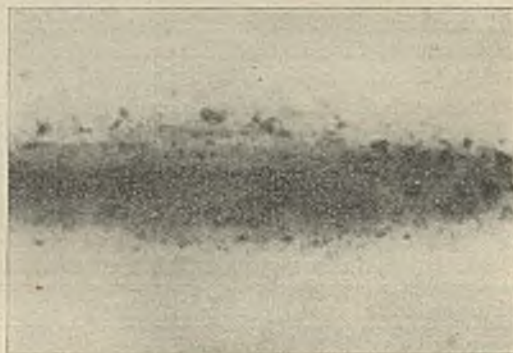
Röntgenaufnahme einer Elektroschweißnaht von 20 mm Blechdicke mit Schlackeneinschlüssen und Poren.
